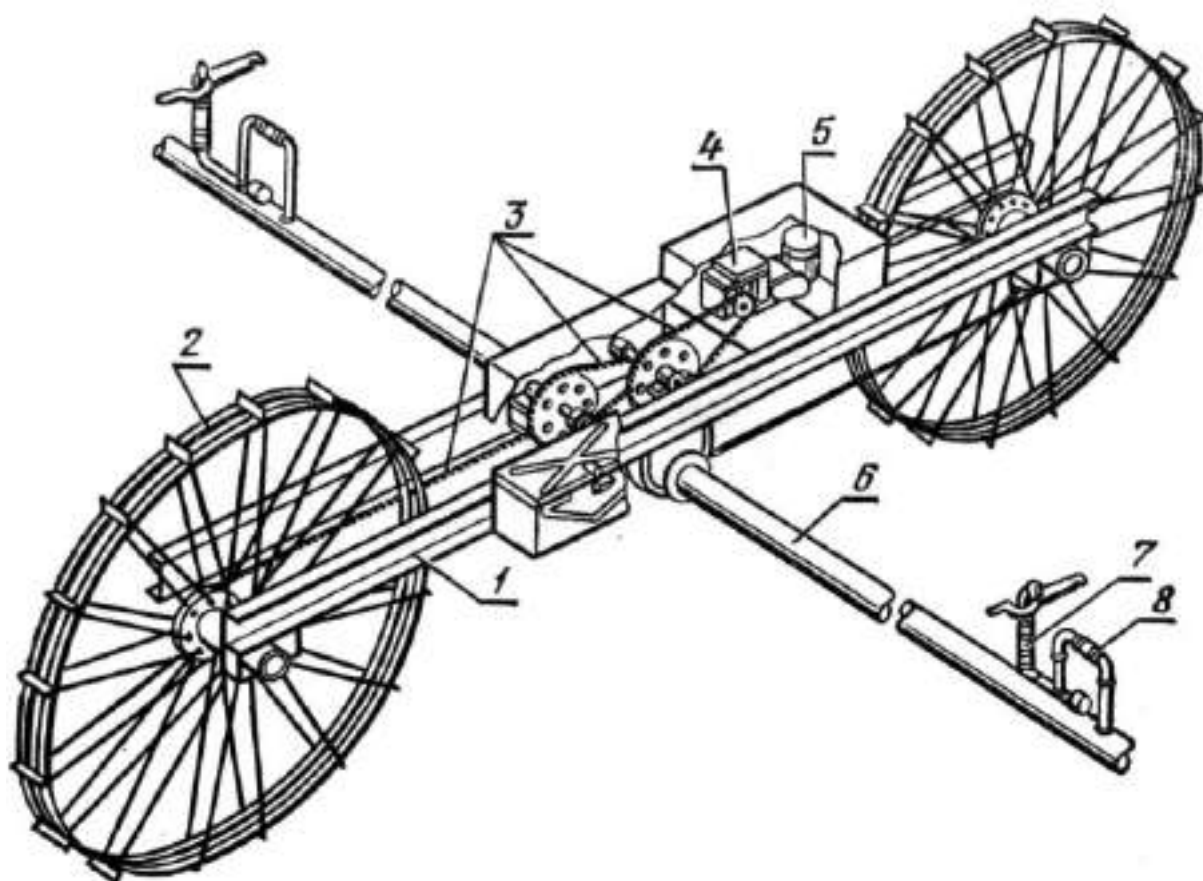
Дождеватель колесный широкозахватный ДКШ-64 «Волжанка»
